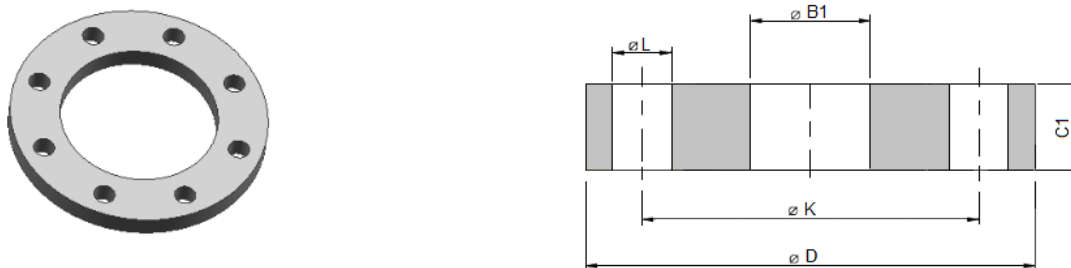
Brida plana EN-1092-1 tipo 1 PN10.
